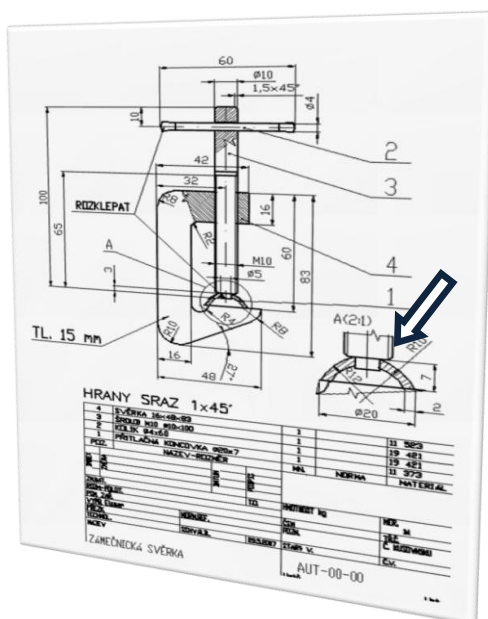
Výkres doplněný detaily. Jsou označeny šipkami. (AutoCAD)
